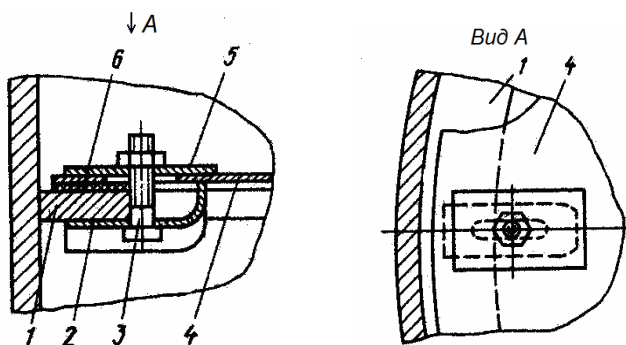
Узел крепления секции тарелки к корпусу аппарата:
